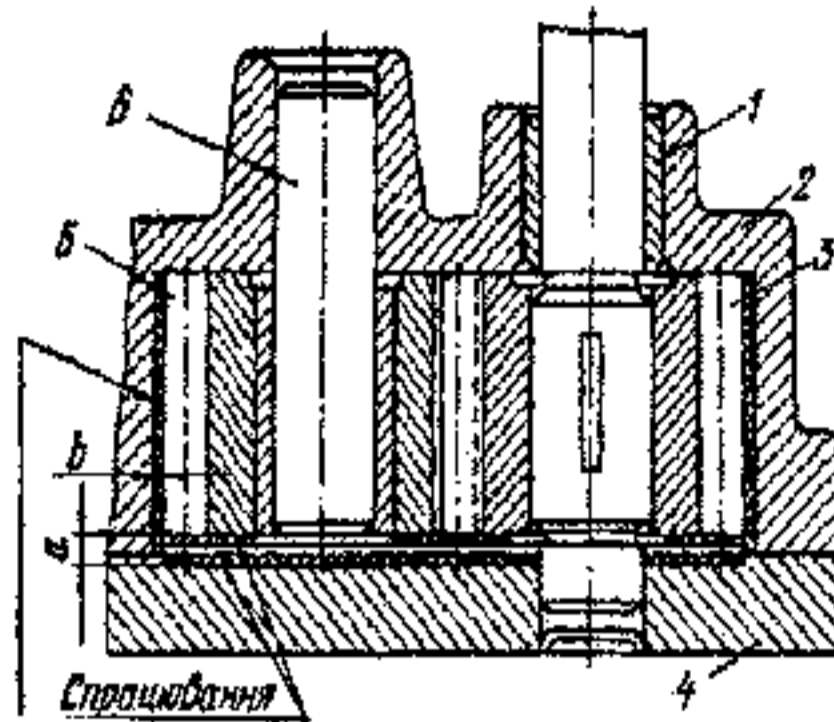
Місця спрацювань корпусу і кришки масляного насоса: 1 - втулка ведучого валика; 2 - корпус; 3 - ведуча шестерня; 4 - кришка (плита); 5 - ведена шестерня; 6 - вісь; а - торцевий зазор; б - радіальний зазор
